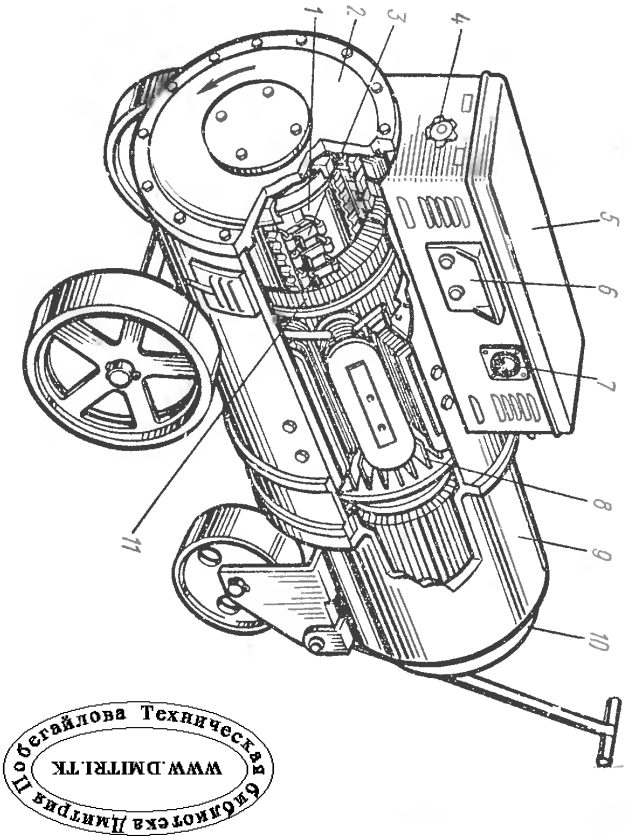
Сварочный преобразователь ПСТ-500-1:
